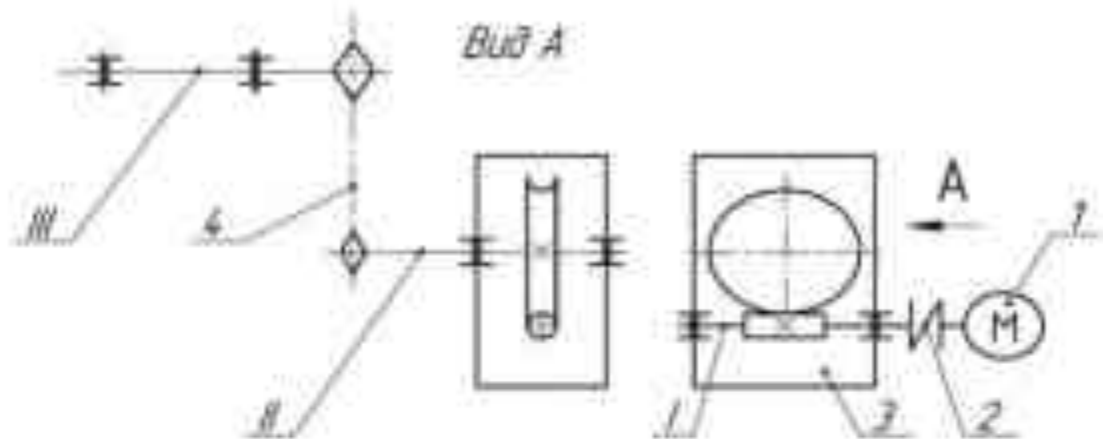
Привід стрічкового конвеєра з мотор-редуктором: 1 – електродвигун; 2 – муфта пружна; 3 – черв'ячний редуктор; 4 – ланцюгова передача; I – провідний вал редуктора; II - ведений вал редуктора; III - вал приводного барабана
